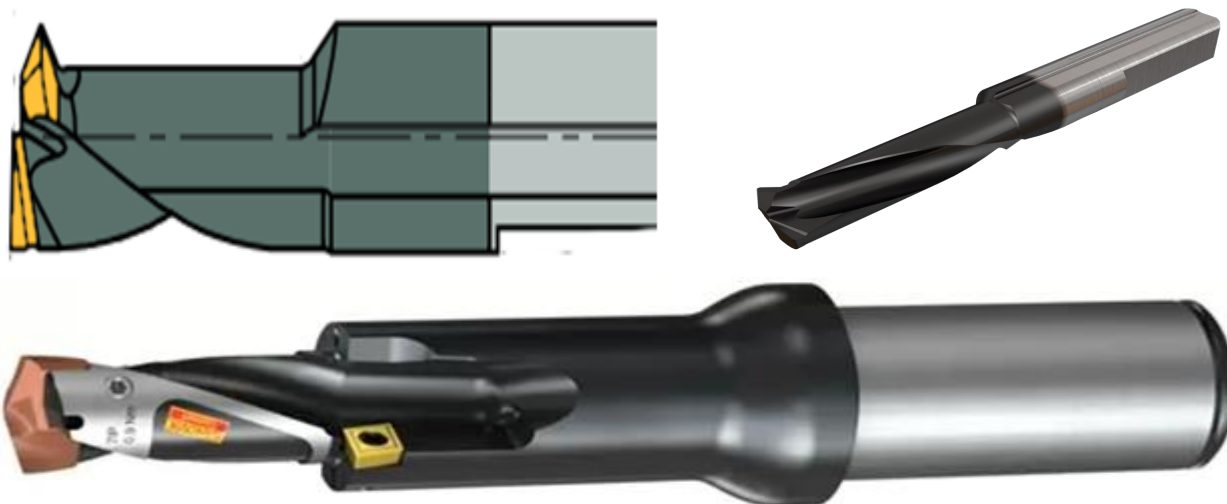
Комбинированный режущий инструмент: сверло-резец-резьбонарезной резец (сверху), сверло-зенкер-зенковка (снизу)
